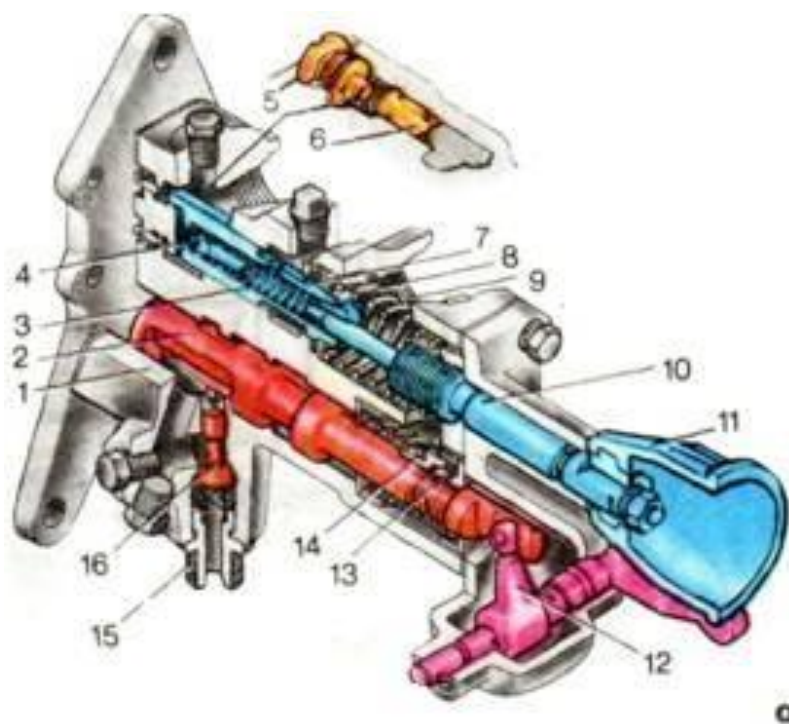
Гидравлический догружатель трактора: а — гидроувеличитель, 1 — корпус, 2 — ползун, 3 — пружина предохранительного клапана, 4 — предохранительный клапан, 5 — канал, соединяющий полости аккумулятора, обратного клапана и ползуна, 6 — обратный клапан, 7 — золотник, 8 — пружина золотника, 9 — отверстия для присоединения трубопровода слива масла в бак, 10 — регулировочный винт, 11 — маховичок, 12 — внутренний рычаг ползуна, 13 — шарик фиксации ползуна, 14 — обойма, 15 — штуцер маслопровода от основного цилиндра, 16 — запорный клапан
